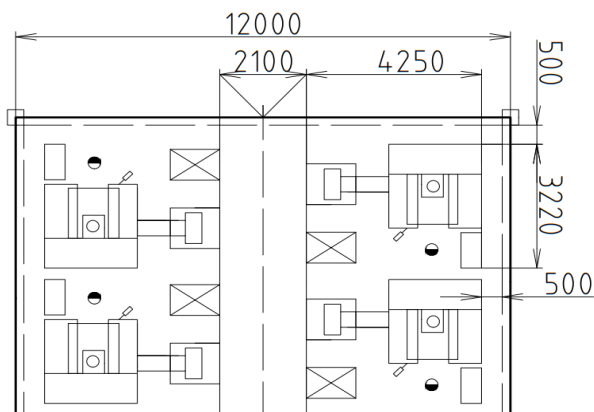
Obráběcí centrum VMC 80/8 B od
